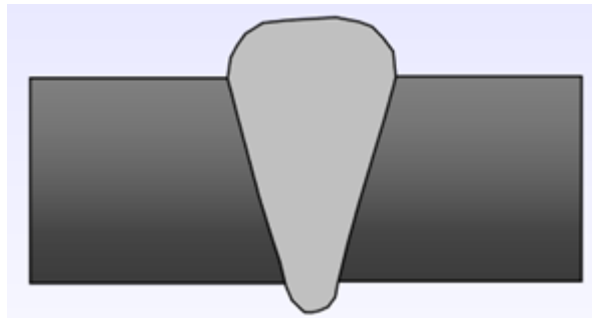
Înălțimea excesivă a capacului. Sursă: M.S. Rogers, Welding Inspection Defects/Repairs Course Reference WIS 5, 2003.
